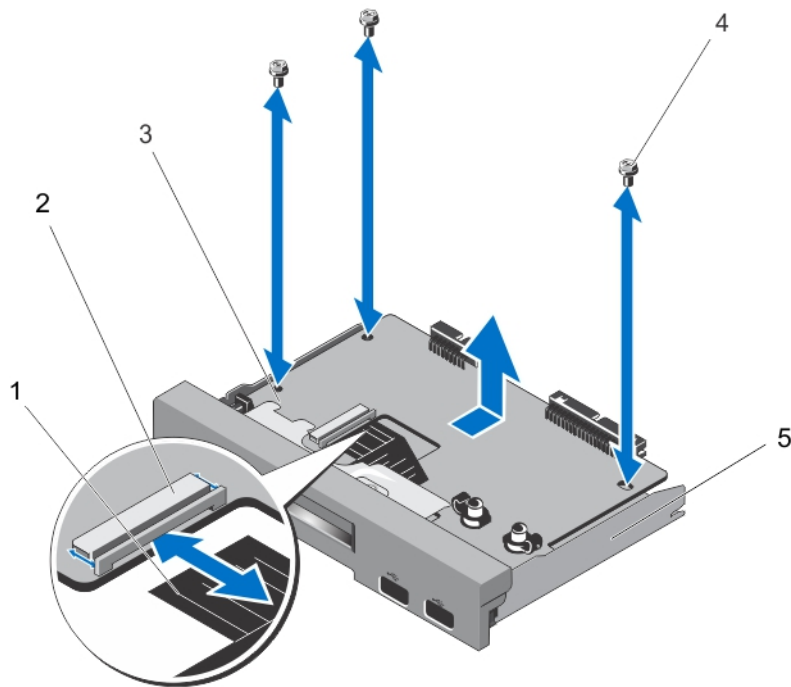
Entfernen und Installieren der Bedienfeldplatine mit LCD-Modul
